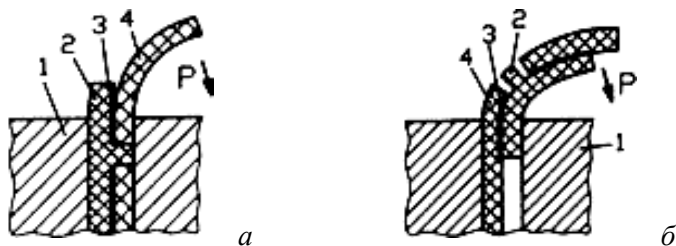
Схема испытания раструбных сварных соединений на отдир: *а* — трубы от раструба соединительной детали; *б* — раструба соединительной детали от трубы; 1 — зажимное устройство; 2 — часть образца, вырезанная из соединительной детали; 3 — сварной шов; 4 — часть образца, вырезанная из трубы
